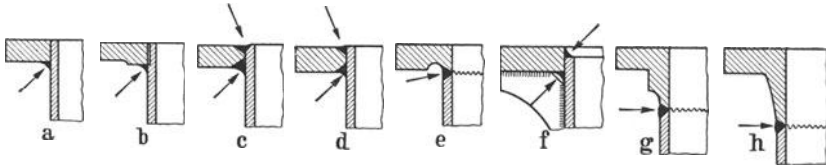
Schweißungen von Rohrflanschen.
